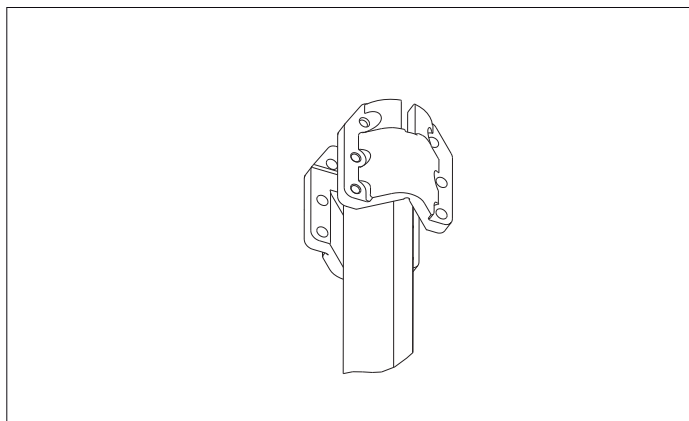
Установка двух полумуфт на вал квадратного сечения
